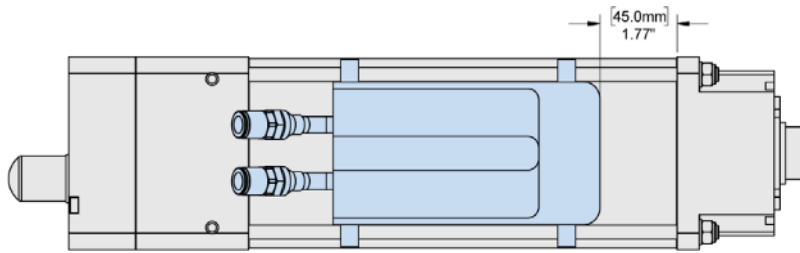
Wasserkühlungsoption 45 mm (1.77") vom Kopf entfernt auf einer beliebigen Seite des ServoWeld-Aktuators anbringen
